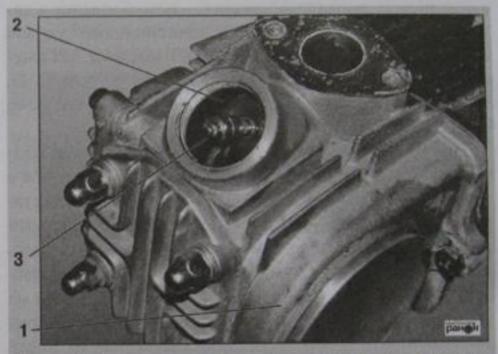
Расположение регулировочного винта зазоров клапанов: 1 – головка цилиндра; 2 – регулировочное отверстие; 3 – регулировочный винт
